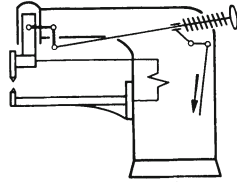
Parallel geführte Oberelektrode für große Ausladung und Elektrodenkräfte. Abb. 55 ··· 56. Elektrodenführung bei Punktschweißmaschinen.
